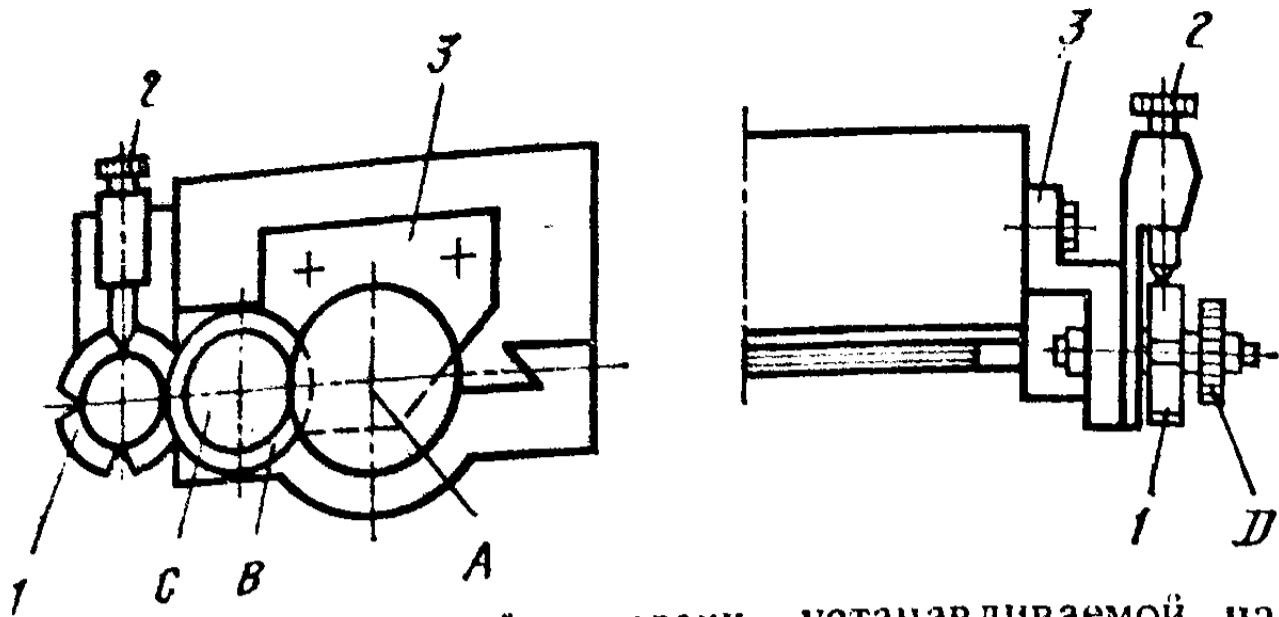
Механизм зубчатой передачи, устанавливаемой на столе фрезерного станка
